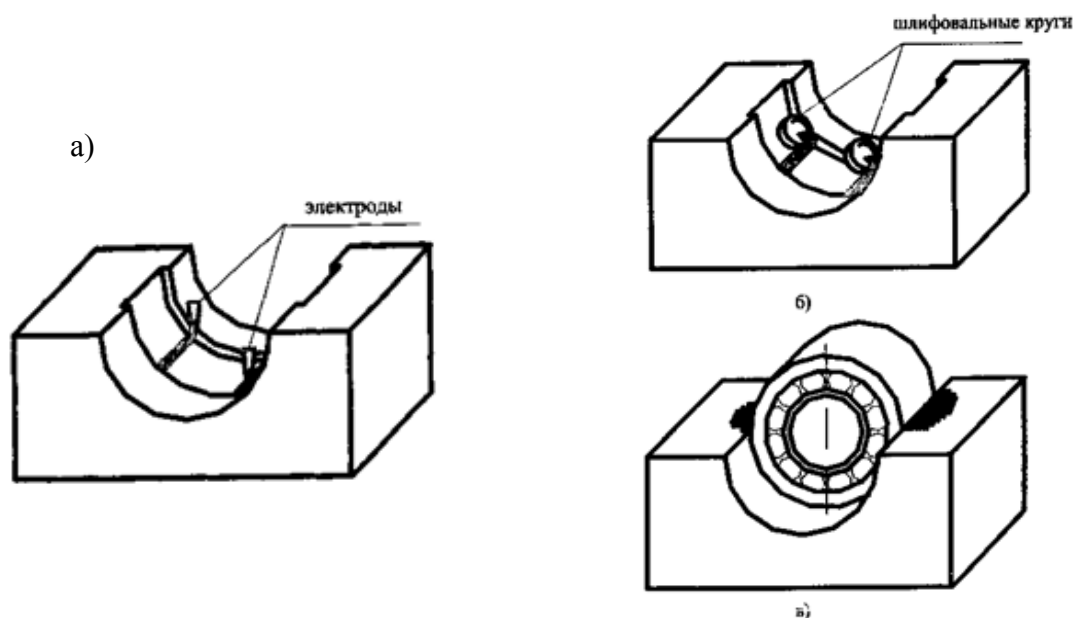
Подготовка, расположение установочных маячков, нанесение материала и установка подшипника в проектное положение: а) наплавка маячков; б) шлифовка до базового размера; в) установка подшипника
